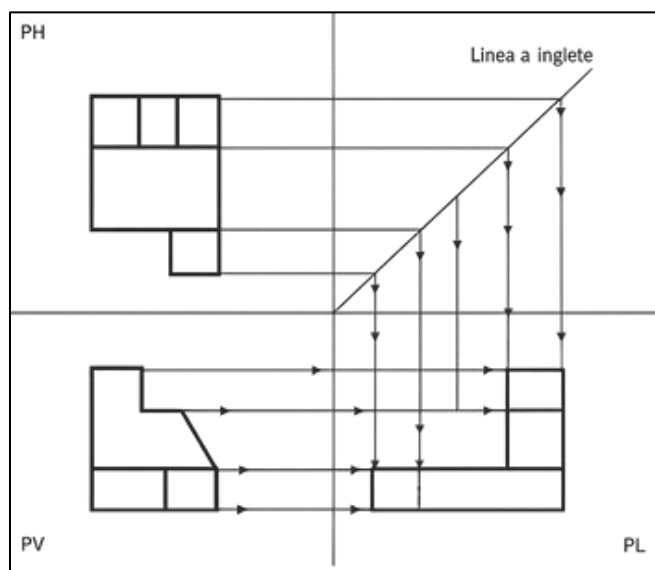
Proyección de vistas sobre los planos de proyección por el método de abatimiento de planos
